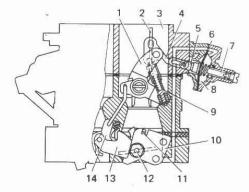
Esquema del dispositivo de arranque del carburador 2107-1107010:
